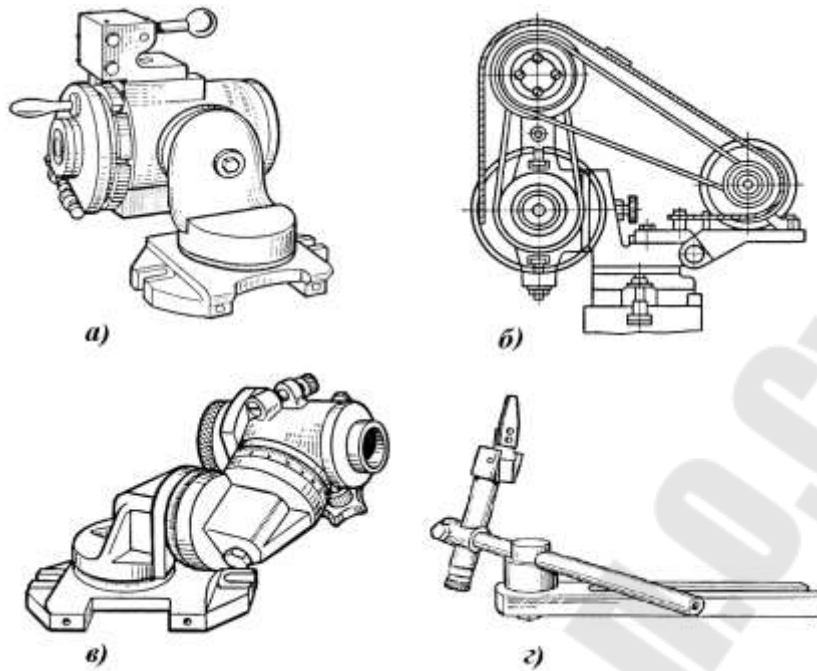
Эскизы основных приспособлений к универсально-заточному станку 3М642:
